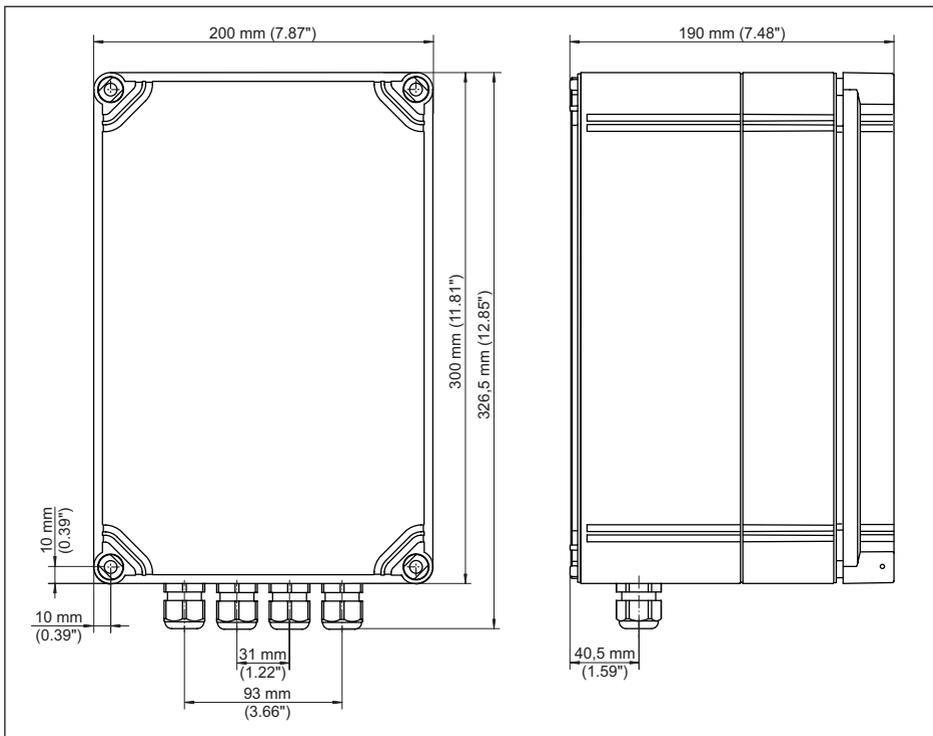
Dimensions ISO-GEH.AXX avec 4 passe-câbles
